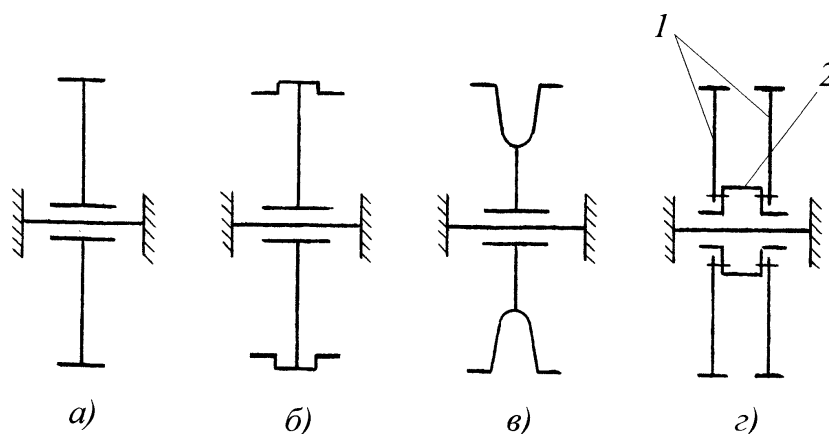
Схемы конструкций ободьев направляющих колес
